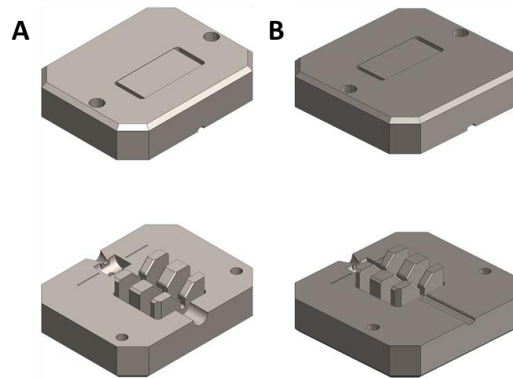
Exemplo de um molde de 30 mm (A) e de 36 mm (B).
